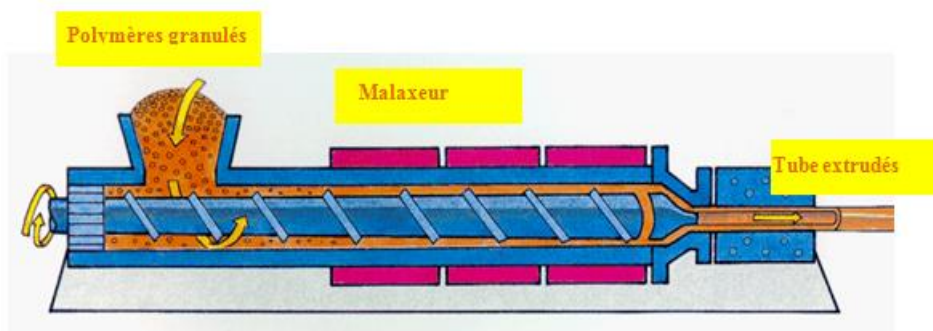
Représentation d'une machine d'extrusion des tubes [28].
